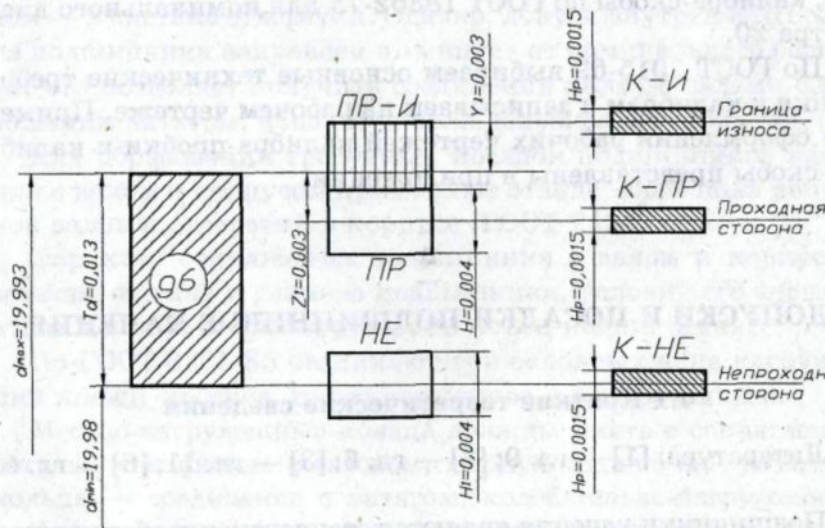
Схема расположения полей допусков калибров для контроля вала  $\varnothing 20$  g6 и контркалибров
